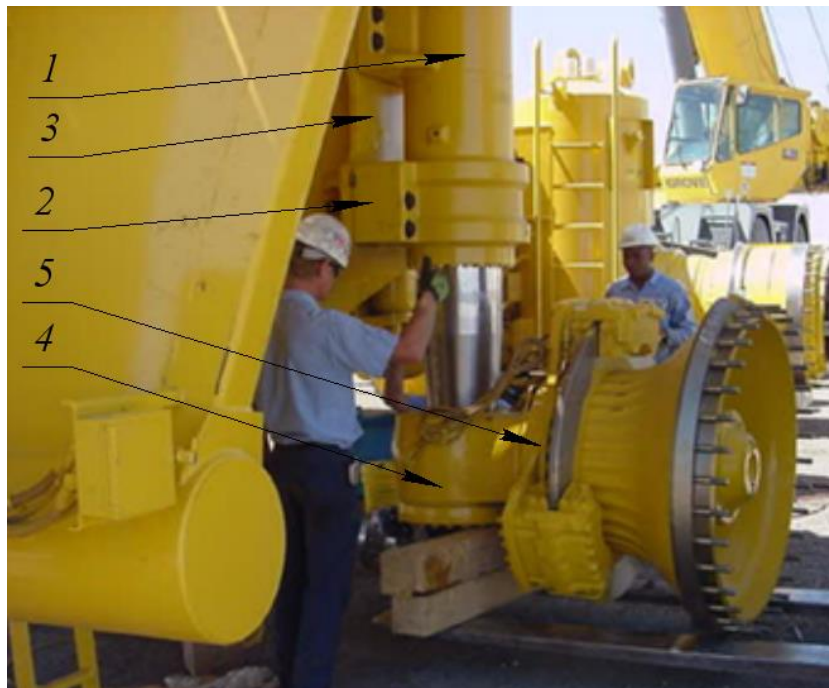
Внешний вид подвески Komatsu 830E. 1 – рама; 2 – узел крепления рамы и цилиндра; 3 – ПГР передней подвески; 4 – поворотный кулак; 5 – ступица
